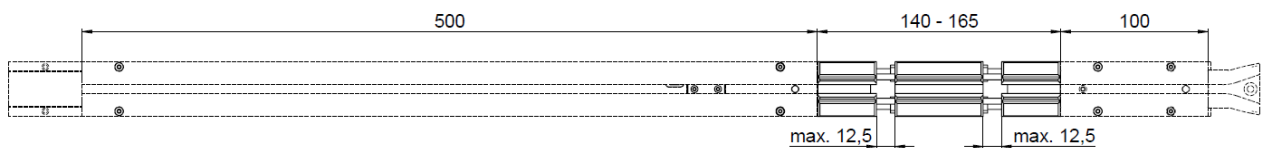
Dehnelement – Endeinspeisung (rechts montiert)
